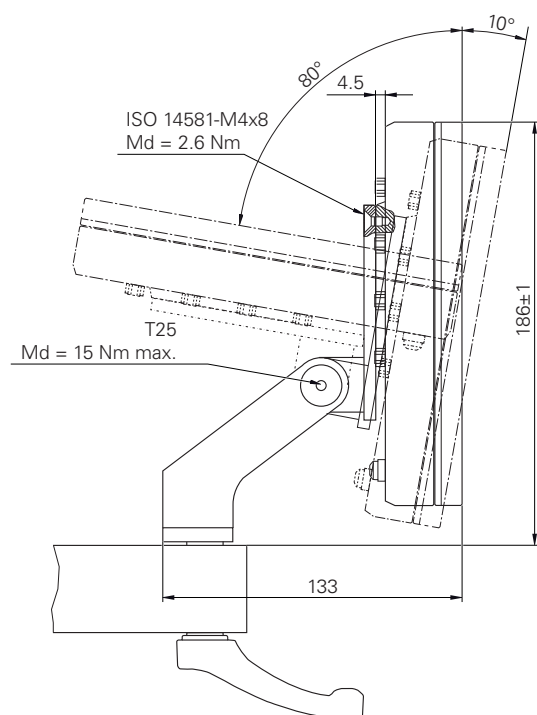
Dimensiones del aparato con soporte Multi-Pos
